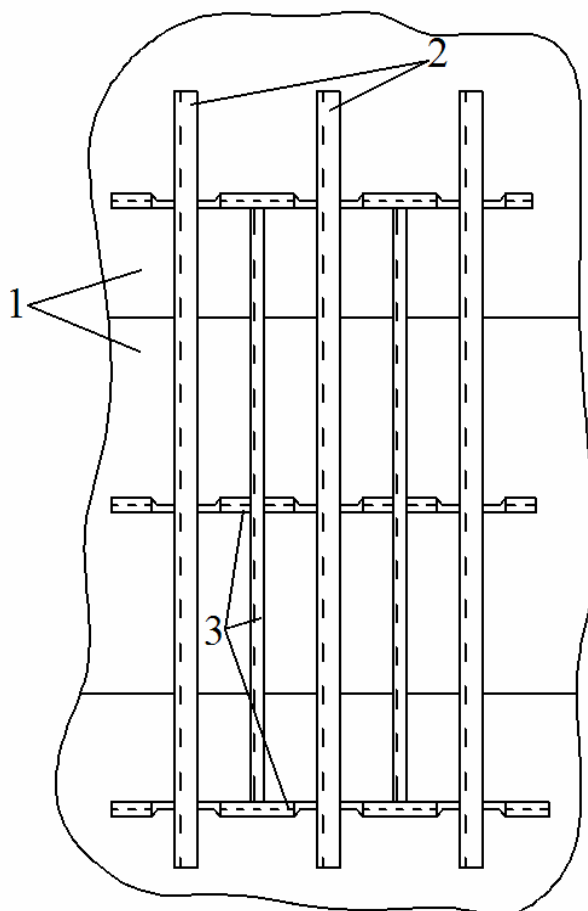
Схема подкрепления изношенной бортовой обшивки (1– пояся обшивки; 2– основные ребра; 3– подкрепляющие ребра).
